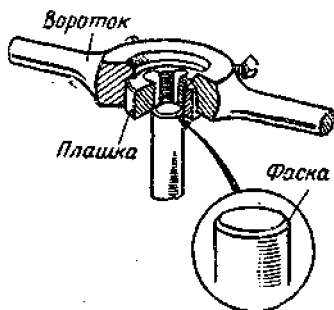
Плашка для нарезки резьбы, установленная в воротке.
